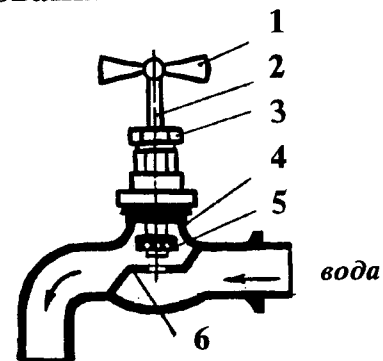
Водопроводный кран: 1 — маховичок; 2 — шпindel; 3 — уплотнительная гайка; 4 — корпус; 5 — шайба с прокладкой; 6 — гнездо
